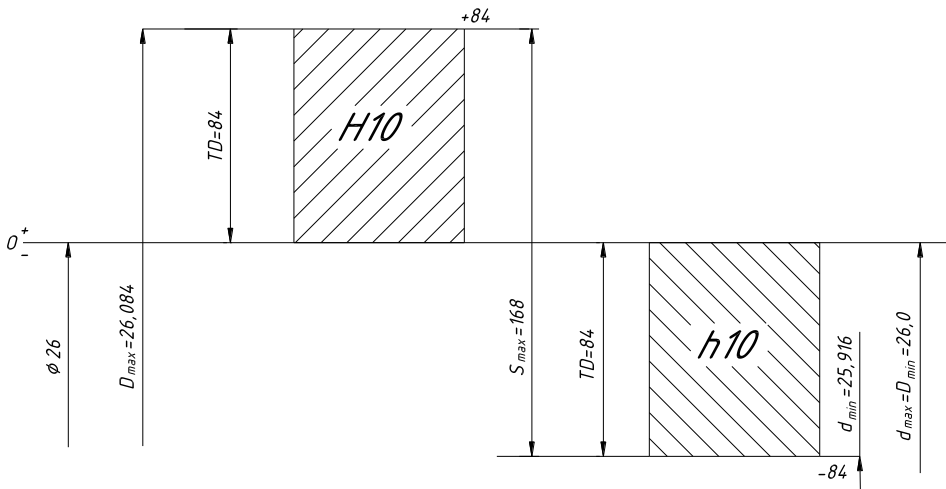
Схема розташування полів допусків з'єднання $\varnothing 26 \frac{H10}{h10}$
